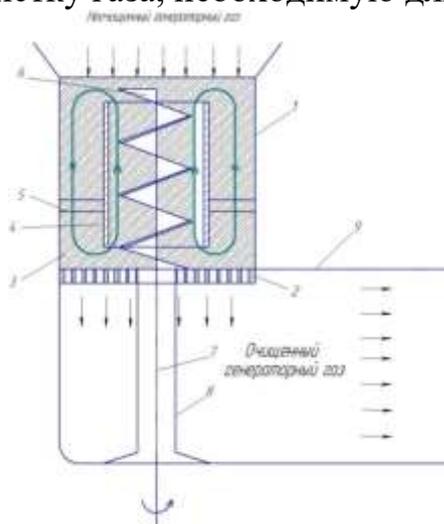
Регенеративный фильтр: 1-цилиндрический корпус; 2-разделительная сетка; 3-фильтрующий элемент (гидроксид алюминия); 4-кожух шнека; 5-металлическая пластина; 6-шнек; 7-вал; 8-корпус вала; 9-трубопровод. [2]
